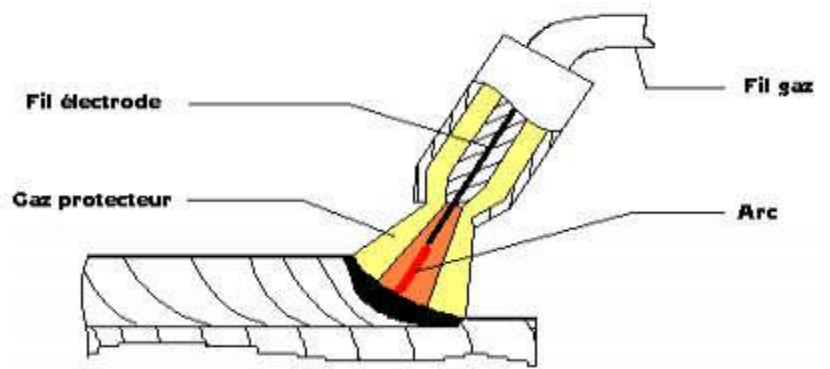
Principe de soudage MIG et MAG [22]
